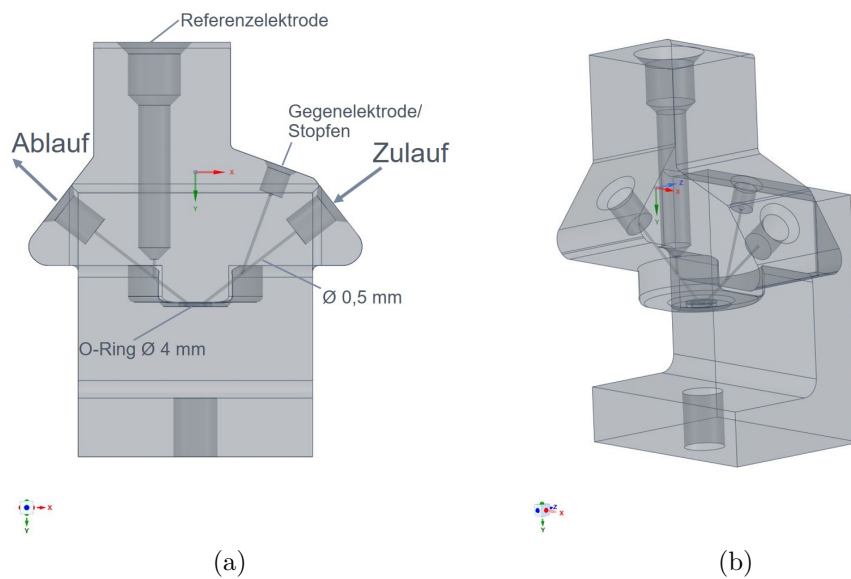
CAD-Modell der Durchflusszelle (a) Frontalansicht (b) Seitenansicht
